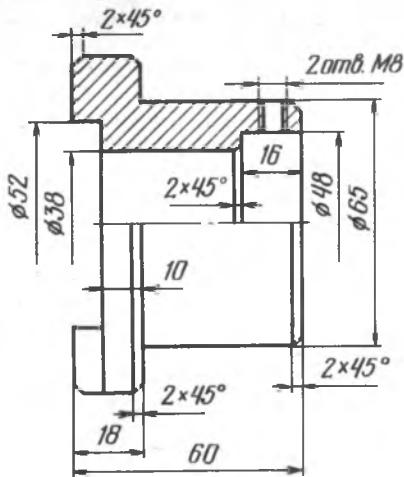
Переходной штуцер к прибору КИ-562 для проверки и регулировки форсунок двигателя «Зетор»
